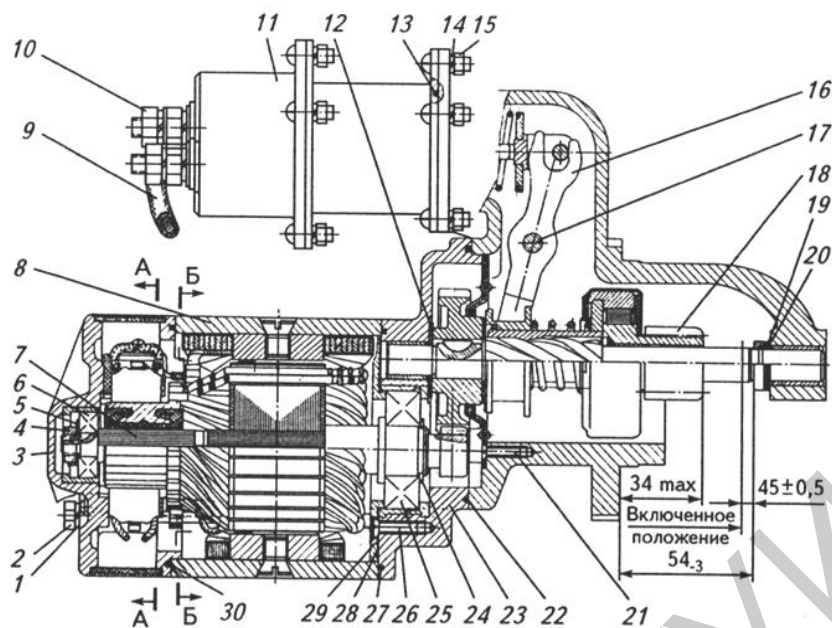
Стартер со встроенным цилиндрическим редуктором с внешним зацеплением:
